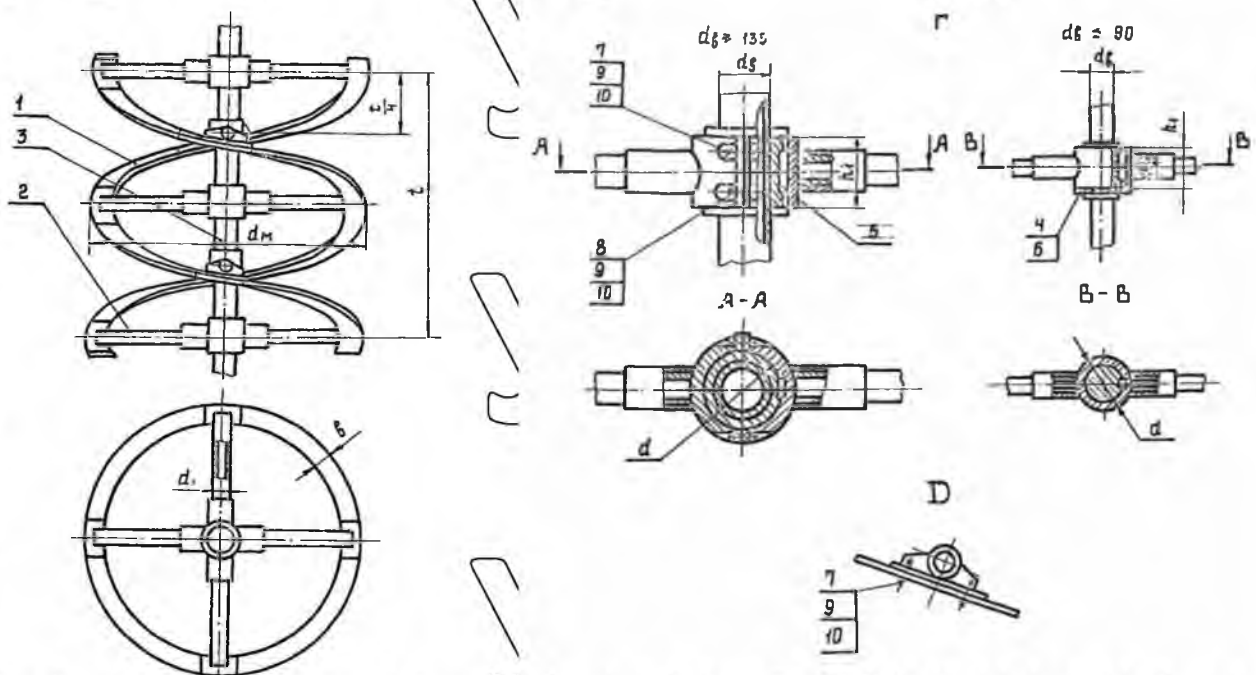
Конструкція стрічкової мішалки типу 11 [2]: 1 – стрічкова лопать; 2 – траверса; 3 – вертикальний вал; 4 – вкладне кільце (із двох частин); 5 – шпонка (ГОСТ 23360); 6 – болт (ГОСТ 7798); 7 – болт (ГОСТ 7818); 8 – болт (ГОСТ 7796); 9 – шайба (ГОСТ 2524); 10 – шайба стопорна (ГОСТ 13463)
